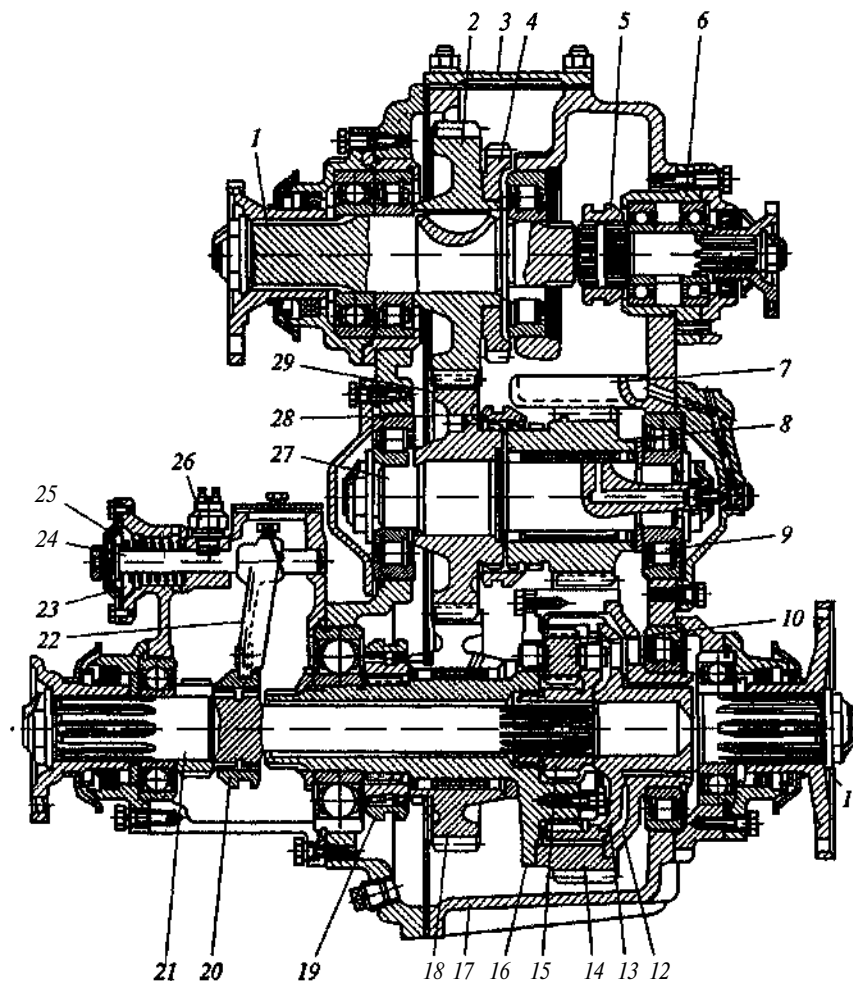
Раздаточная коробка полноприводного грузового автомобиля КамАЗ:
